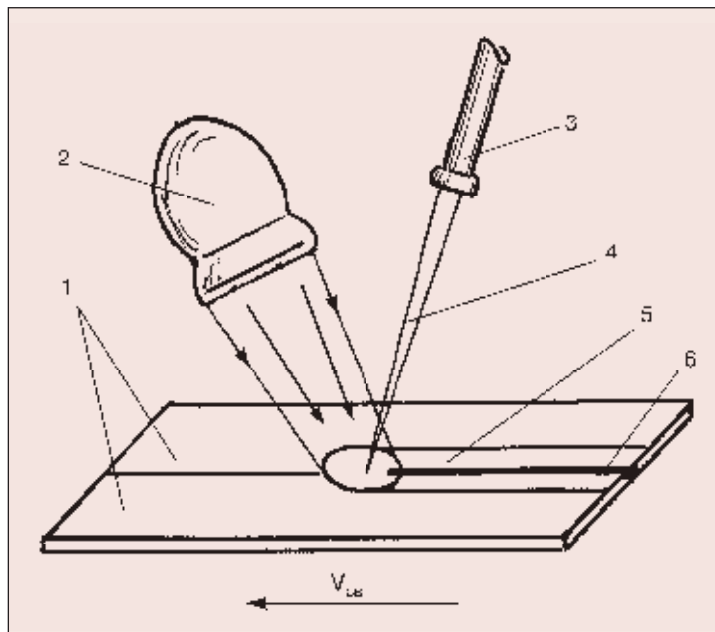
Схема светолучевой гибридной сварки: 1 — свариваемые пластины; 2 — рефлектор светового источника; 3 — лазерная головка; 4 — лазерный пучок; 5 — зона нагрева металла световым источником; 6 — сварной шов
